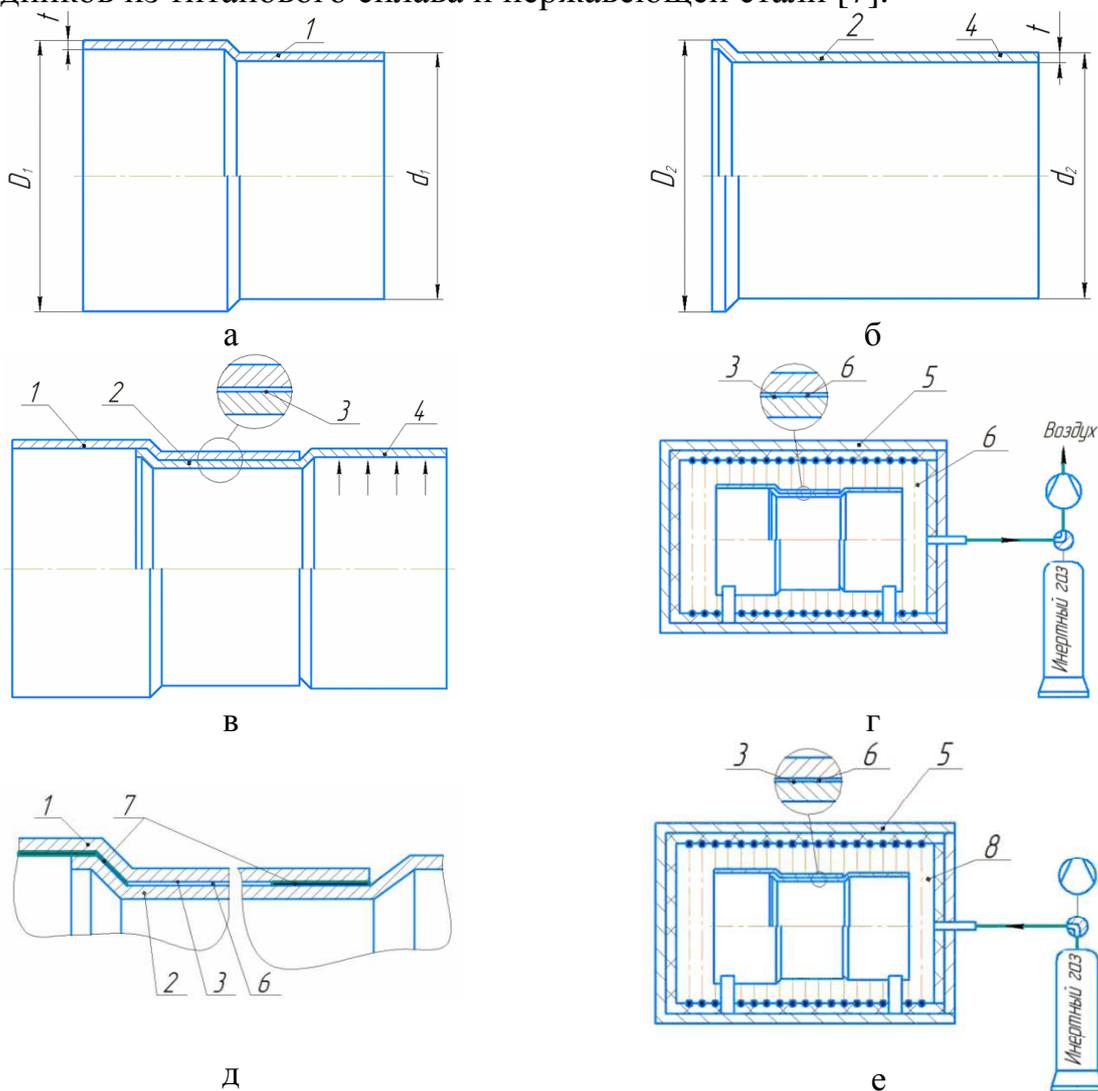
Способ изготовления тонкостенных цилиндрических переходников из титанового сплава и нержавеющей стали: а – трубчатая деталь переходника из титанового сплава; б – трубчатая деталь переходника из нержавеющей стали; в – соединение трубчатых деталей переходника; г – откачка воздуха с образованием вакуума, нагрев и выдержка при температуре рекристаллизации титанового сплава; д – блокировка технологического зазора оксидными пленками; е – заполнение контейнера инертным газом, нагрев и выдержка при температуре диффузионной сварки до образования диффузионно-сварного соединения
